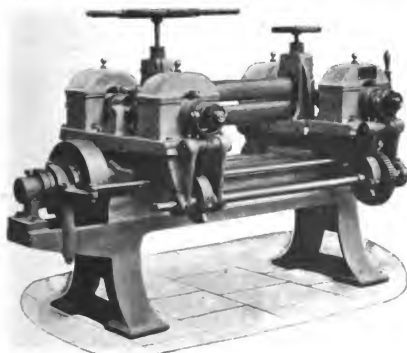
Fräsmaschine für Radiatoren von Collet & Engelhard.
